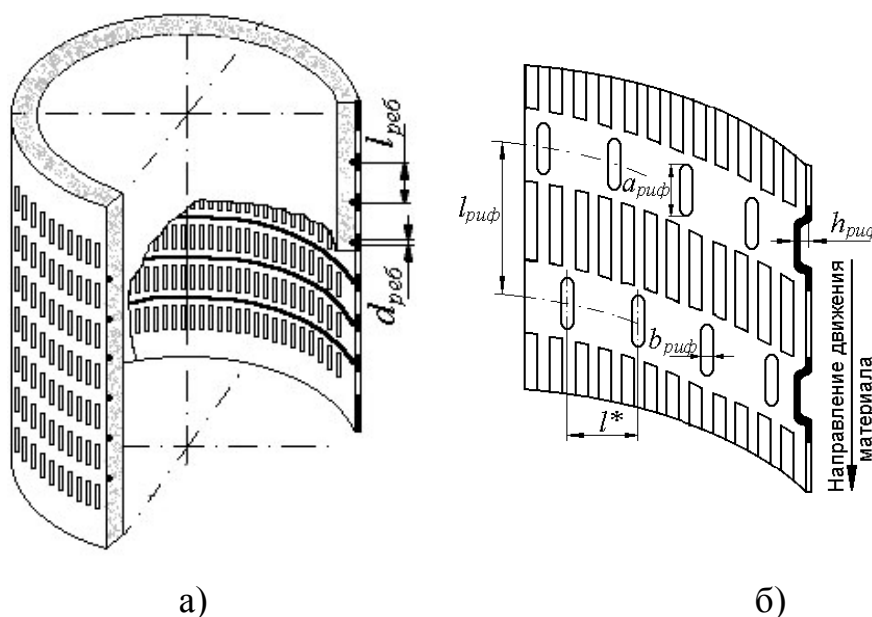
Конструктивные схемы цилиндрических решет с разрыхлителями: а – ребрами; б – рифлями
